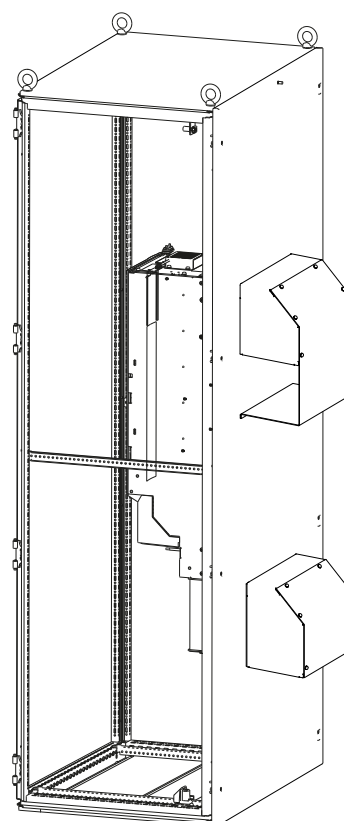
Recorte da Vista Lateral do Gabinete
